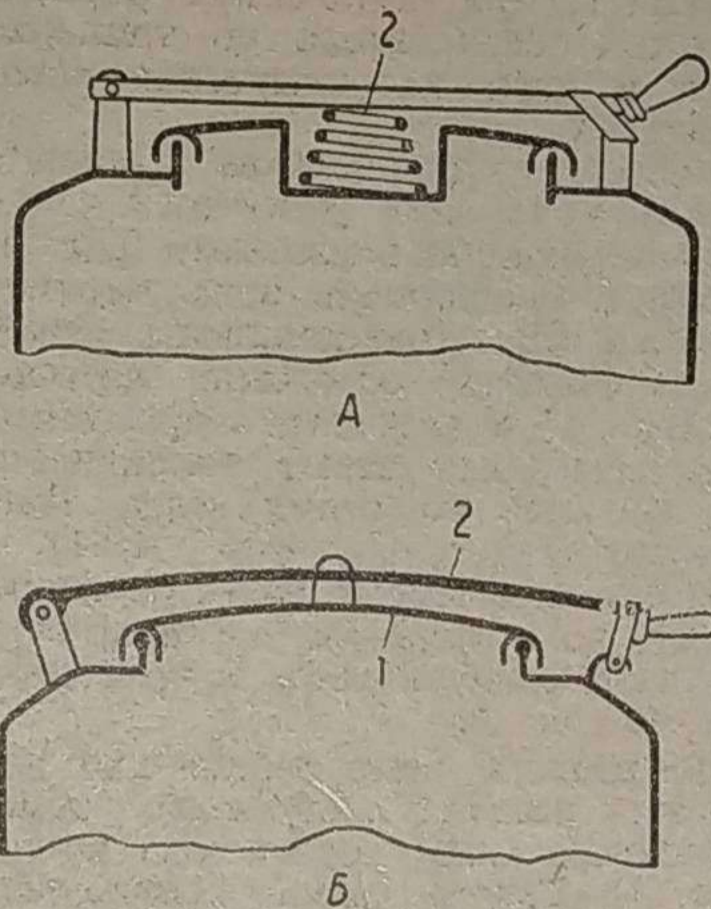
Схема устройства пружинного нажима крышки загрузочного люка
